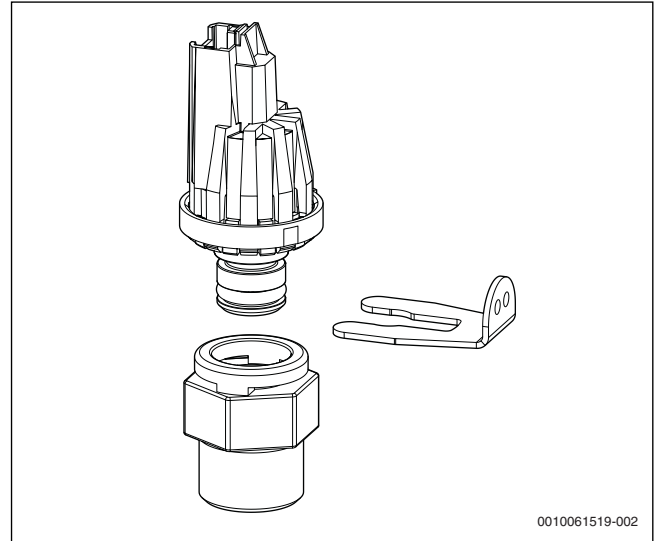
Montage des Druckfühlers JCO über R1/2"-Adapter
